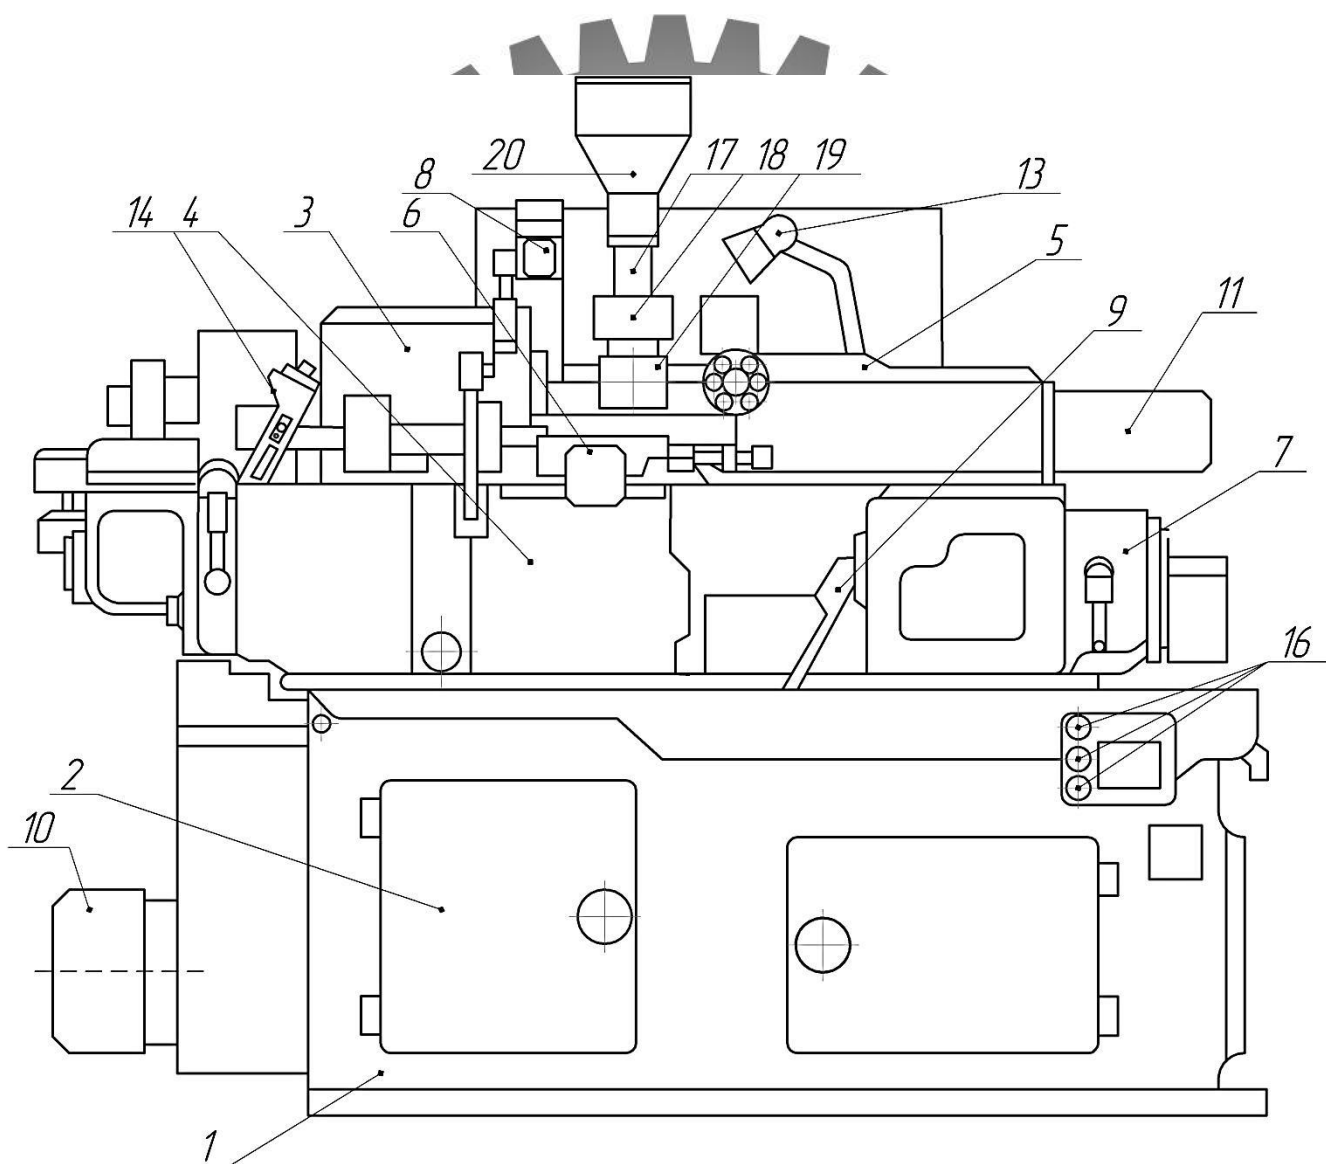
Загальний вигляд верстату з пристроєм для завантаження штучних заготовок
